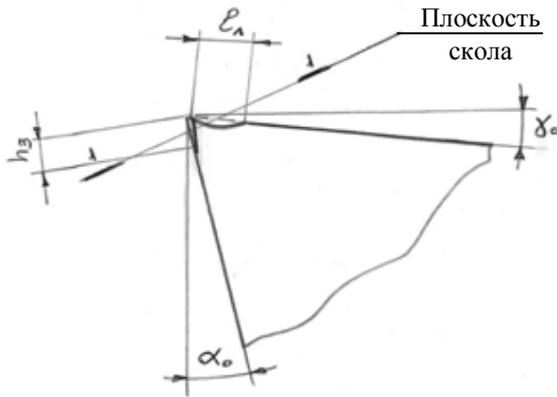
Схема образования фаски и лунки износа, приводящие к сколам режущей кромки инструмента
